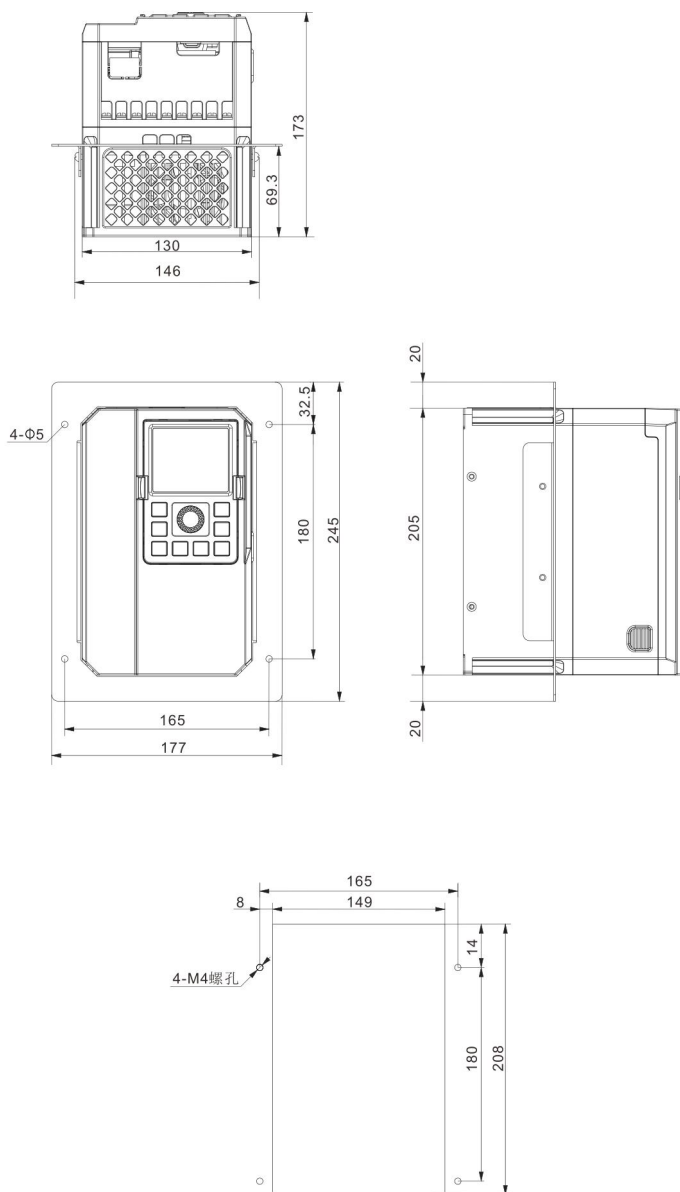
SIZE B (4.0-5.5kw) 机型开孔尺寸
